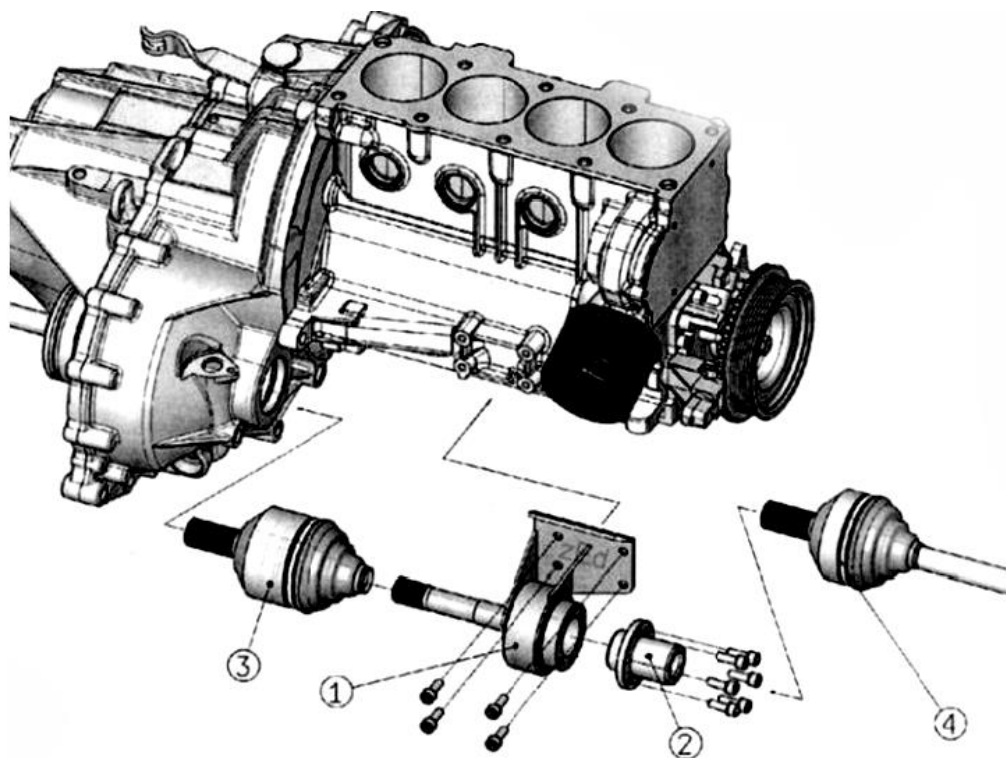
Схема установки промежуточного вала на автомобиль Лада Калина
